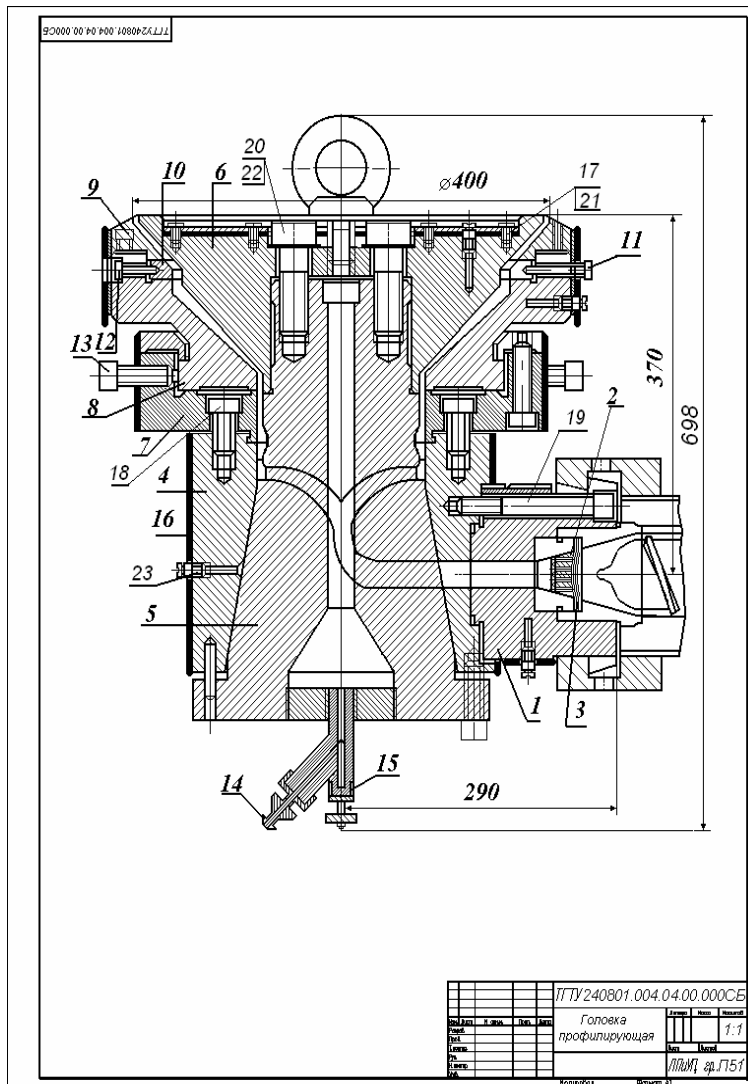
Сборочный чертеж головки профилирующей (вторая проекция изображается на втором листе со штампом высотой 15 мм)
